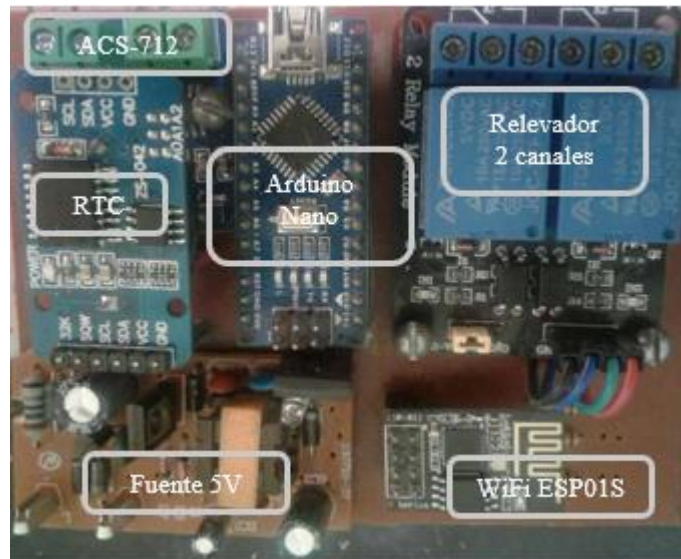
Elementos electrónicos soldados a la placa de cobre.
